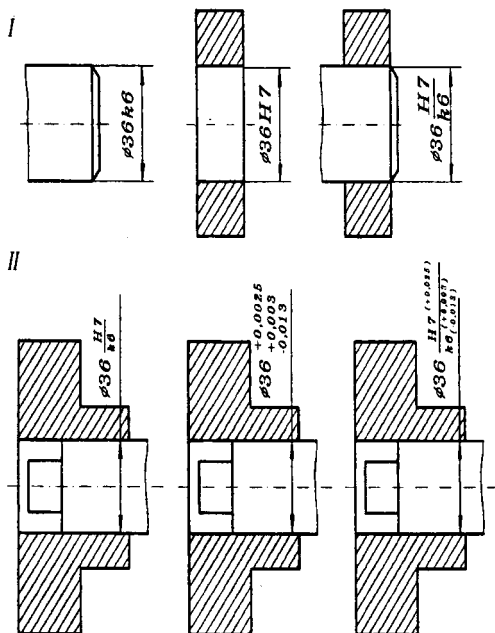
Примеры простановки размеров, допусков и посадок на чертеже
